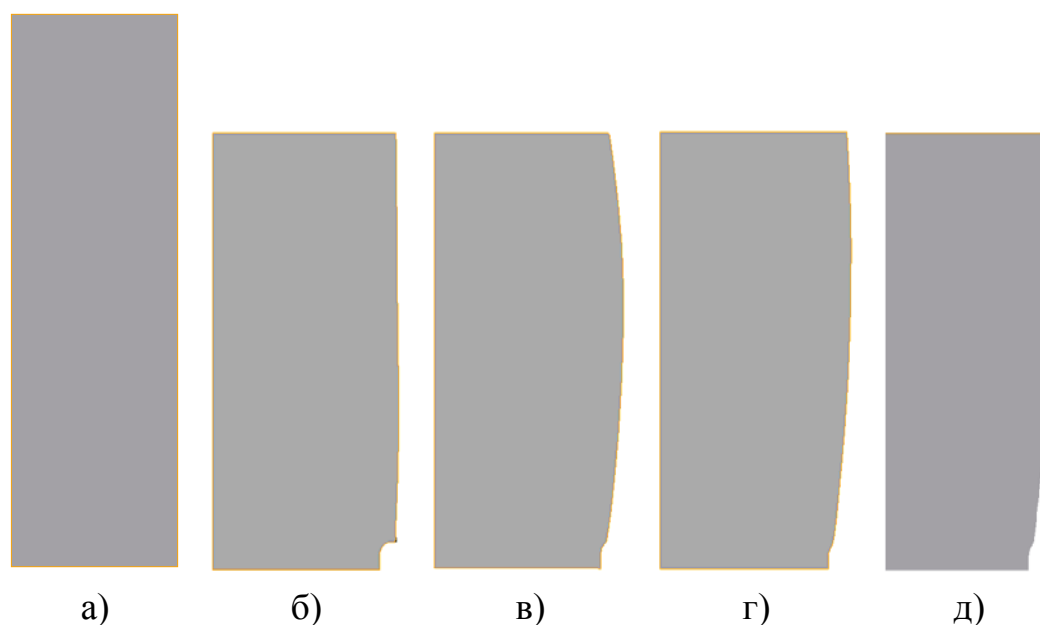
Форма осаженных образцов (показаны половины заготовки и образцов)
